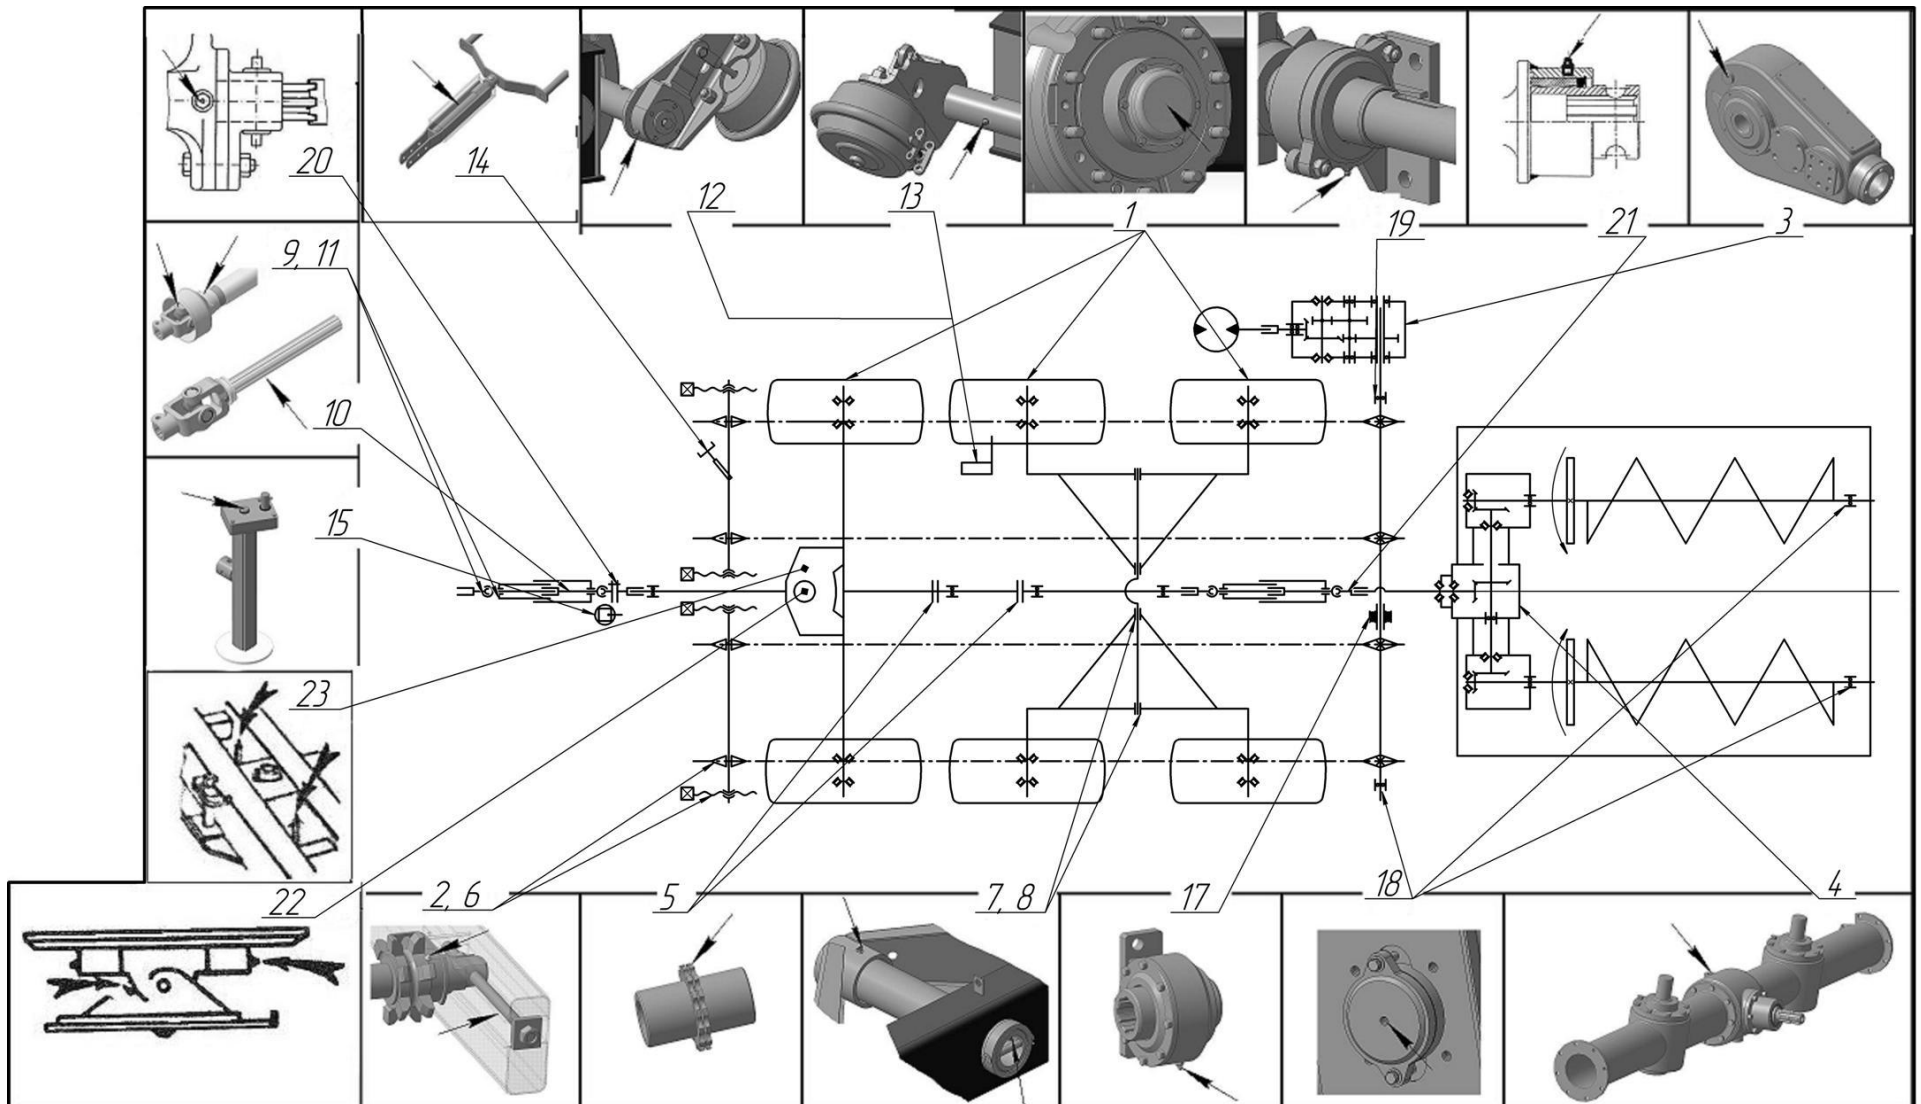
Схема смазки (машина МТУ-24А с разбрасывателем с двумя вертикальными барабанами)
